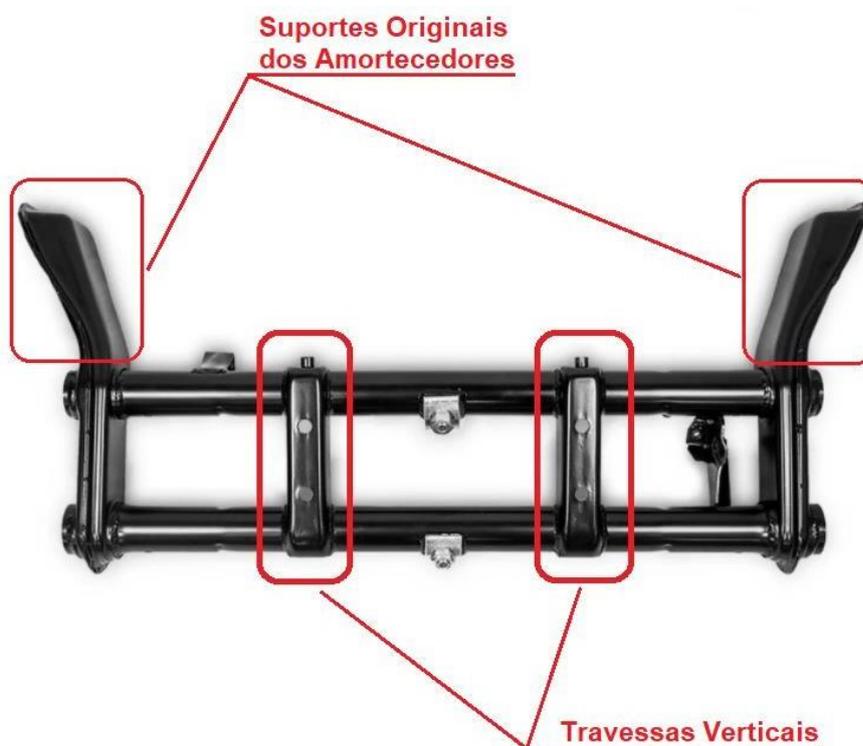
Identificação das travessas verticais e suportes originais dos amortecedores.
